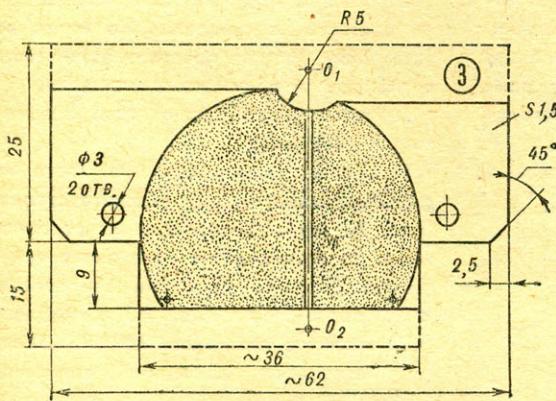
Изготовление подвижной пластины диффконденсатора:
